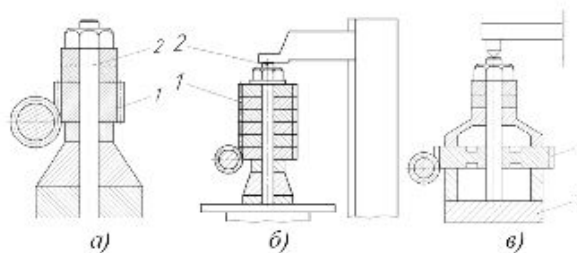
Типовые способы крепления заготовок на зуборезных станках:
